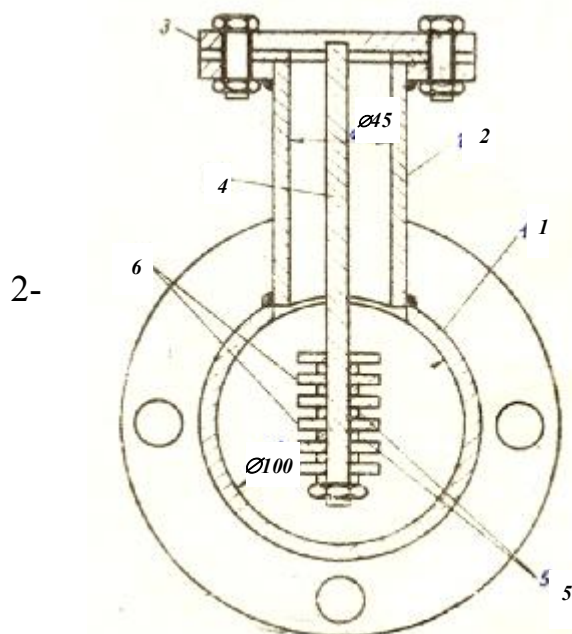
Устройство для установки купонов в проходном сечении байпасной трубы 1-байпас; патрубков с фланцем; 3-заглушка; 4-держатель; 5-прокладки; 6-индикаторы
